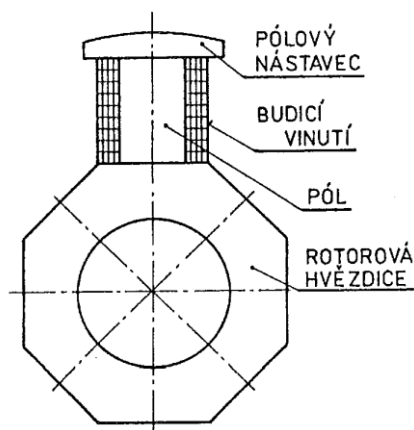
Řez rotorem turbogenerátoru (převzato z [1])
